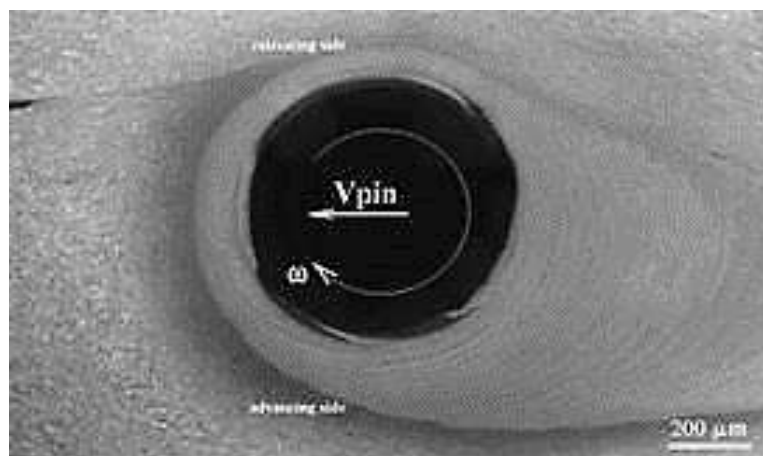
Процесс формирования шва при СТП алюминиевого сплава
